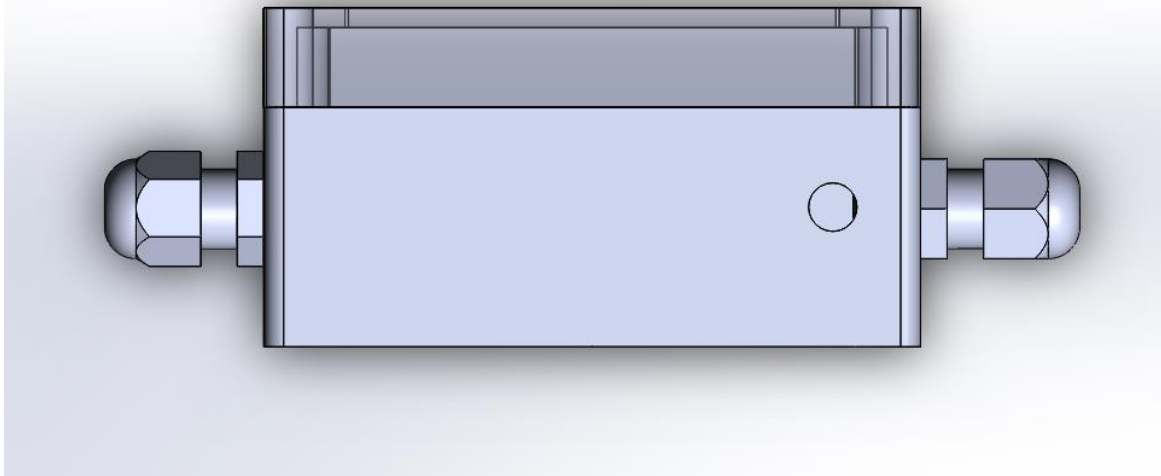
3D модель конструкції (вид зпереду)
